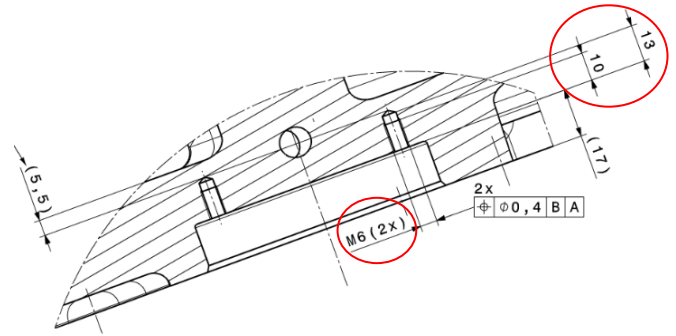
Schnitt B - B durch Bohrungen im Kurbelgehäuse
